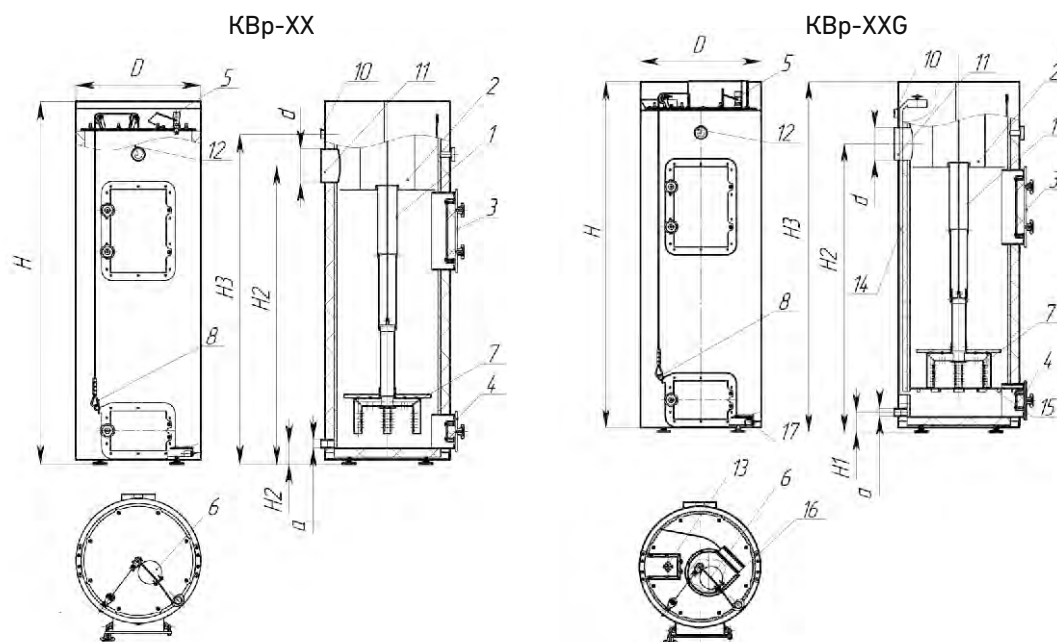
Габаритные и присоединительные размеры котлов KBp (1 – телескопическая труба подачи воздуха, 2 – камера подогрева воздуха, 3 – проем для загрузки дров, 4 – проем для удаления золы, 5 – терморегулятор, 6 – устройство для регулирования подачи воздуха, 7 – распределитель воздуха, 8 – трос, 10 – патрубок подачи воды, 11 – дымоход для отвода дымовых газов, 12 – термоманометр, 13 – регулятор подачи воздуха под колосниковую решётку, 14 – воздуховод, 15 – колосниковая решётка, 16 – воздушный короб с вентилятором).
